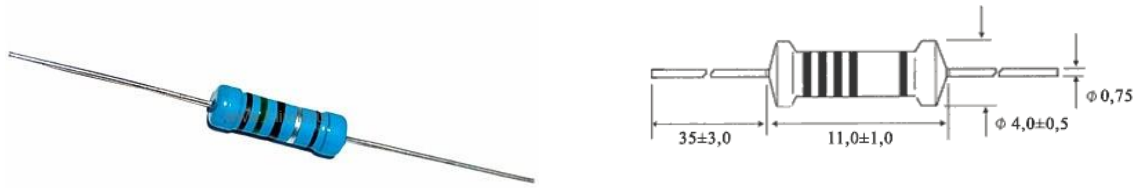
Габаритні розміри постійного резистора типу MF-100
